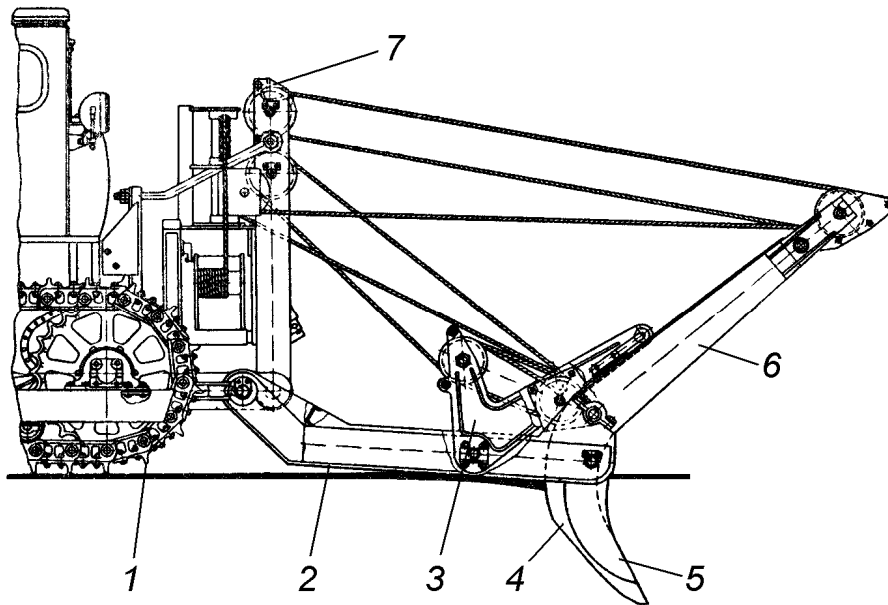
Корчеватель рычажного типа с канатно-блочным приводом корчующего оборудования:
